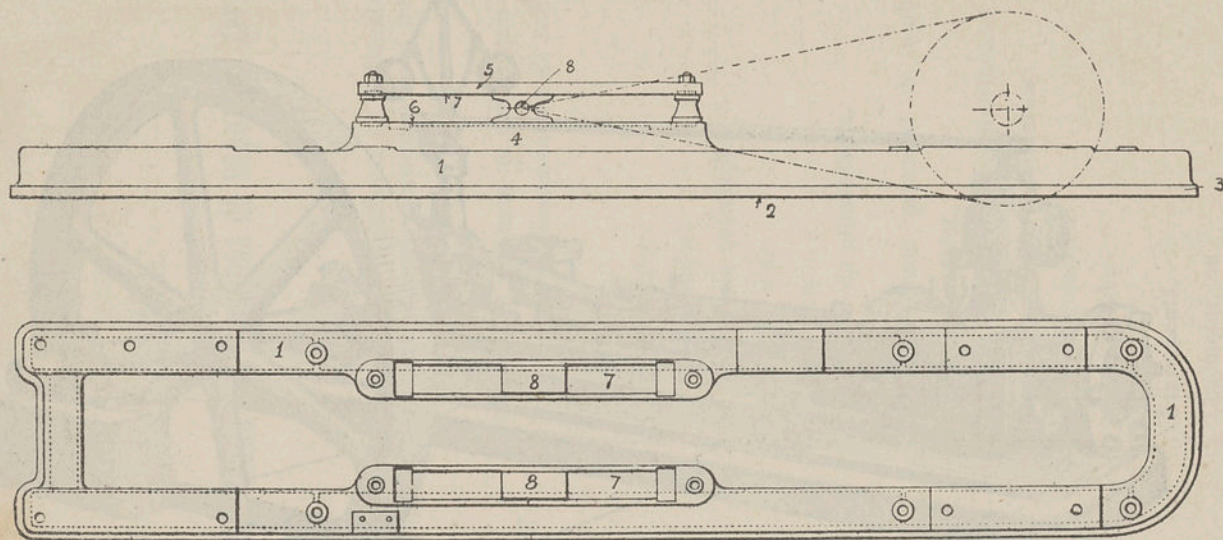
SUPORTE PARA UMA MACHINA HORIZONTAL
